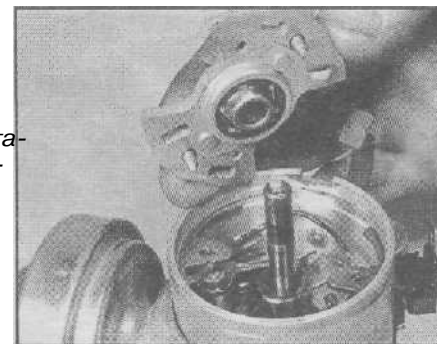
Снятие пластины подшипника - двигателя 1,05 и 1,3 литра
